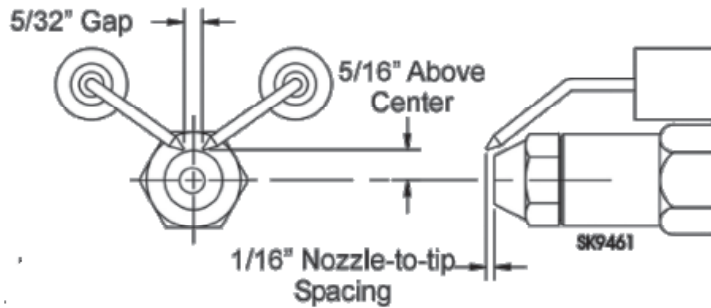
Réglages de pointe d'électrode Beckett, régulateurs de dimensions standard (L2)
